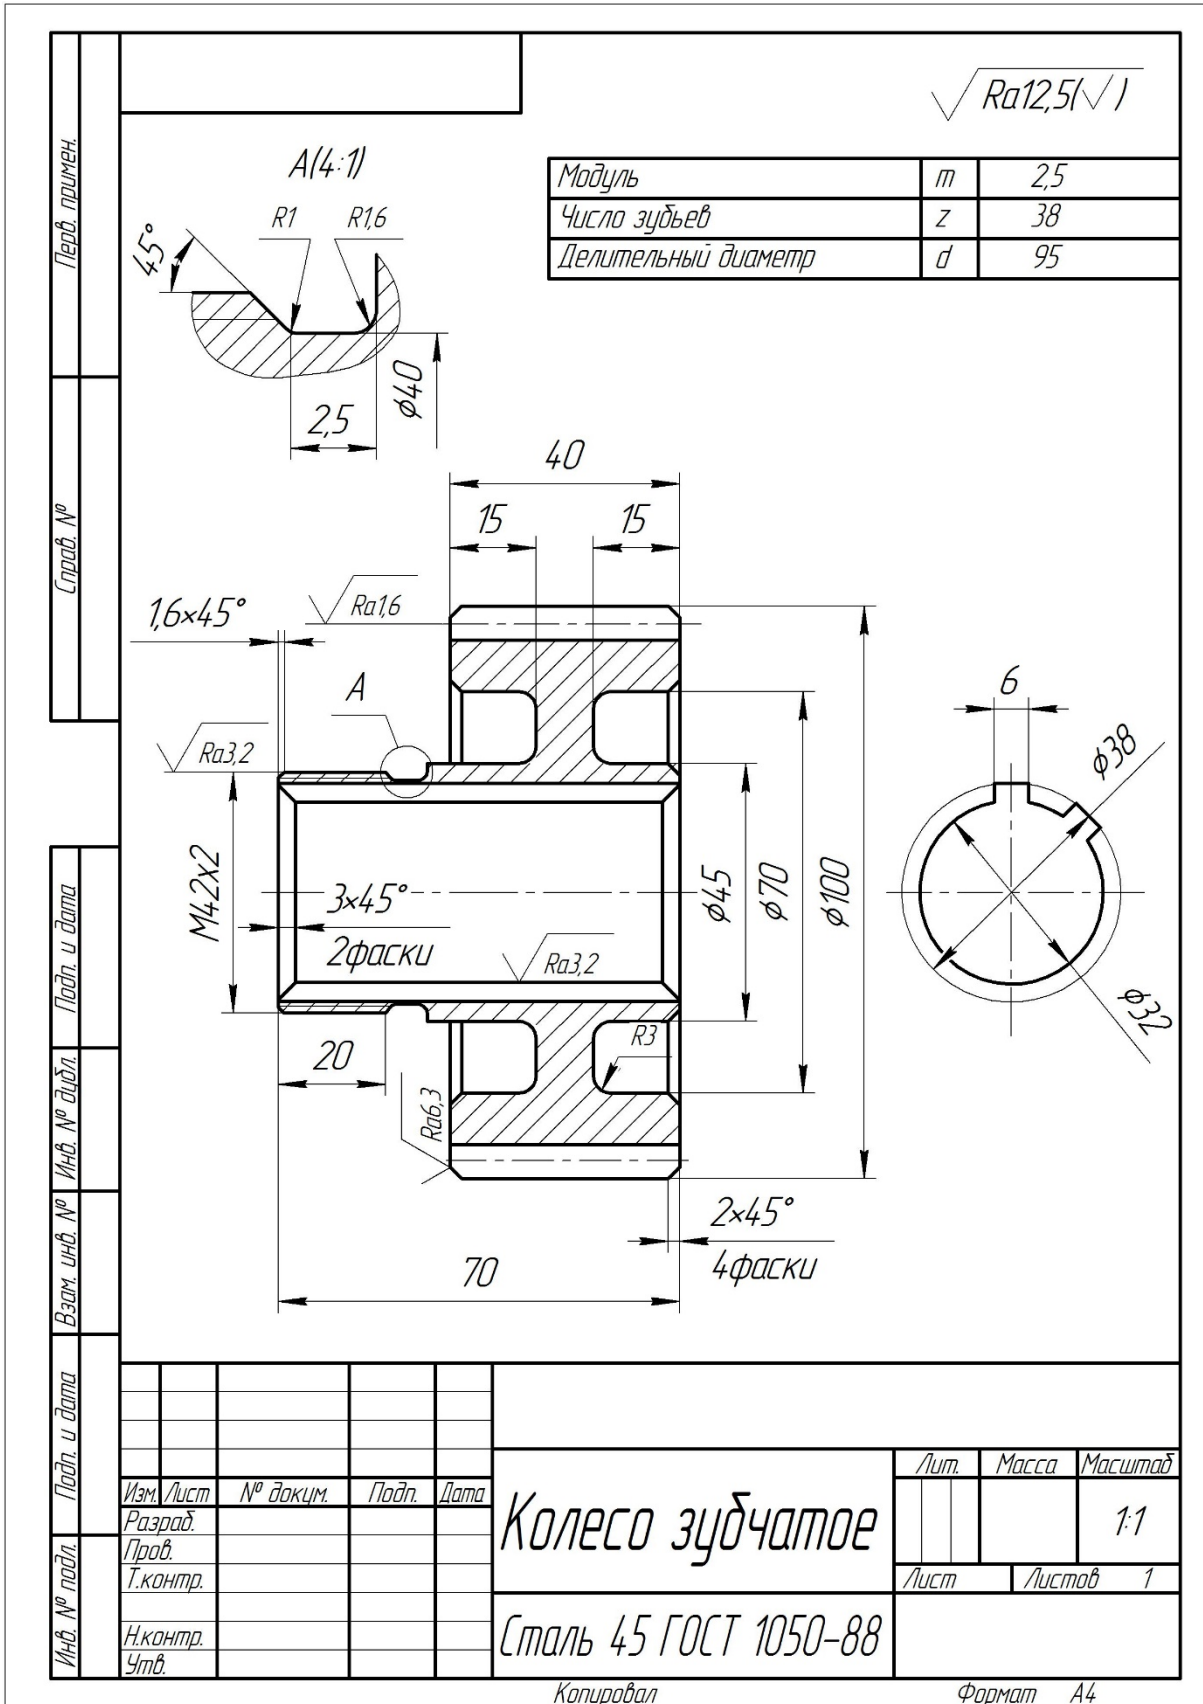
Пример рабочего чертежа зубчатого колеса
